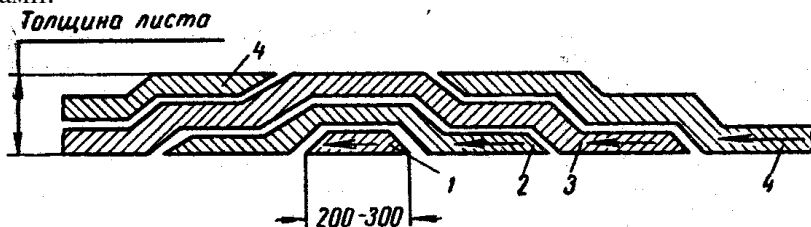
Схема сварки длинных многослойных швов «горкой»:
